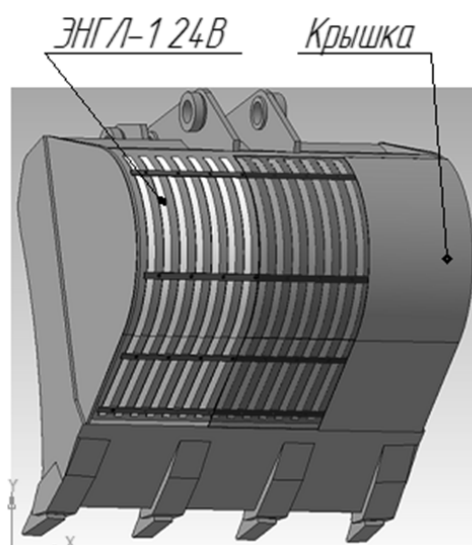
3D-модель ковша экскаватора ЭО-3322 с гибкими электронагревательными элементами ЭНГЛ-1
